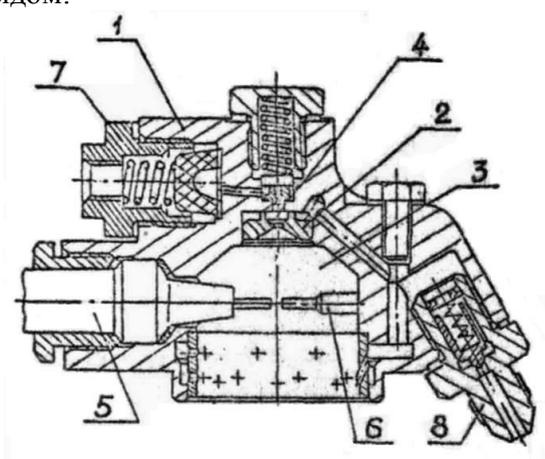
Схема устройства АФП двигателя 5ТДФ [С.216, 5]. Принятые обозначения:
